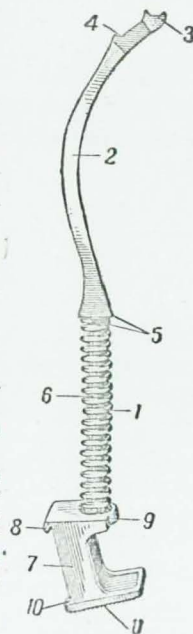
Боевая пружина с толкателем и защелкой магазина:
